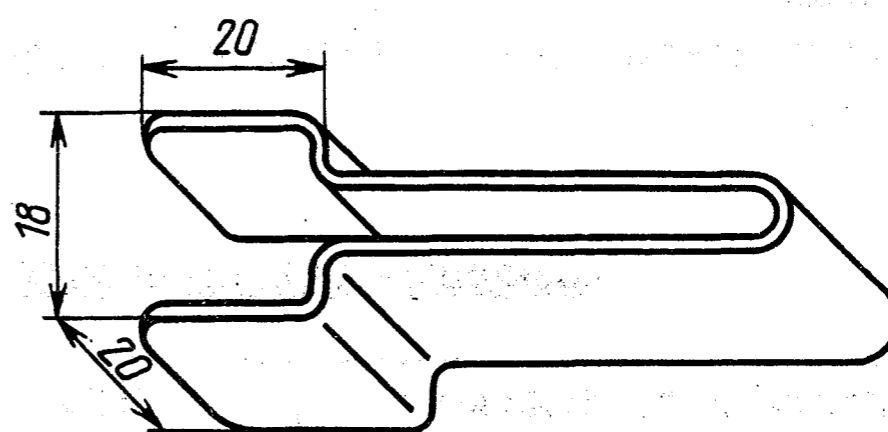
Приспособление для демонтажа верхнего ворсотканевого желобка из двери
